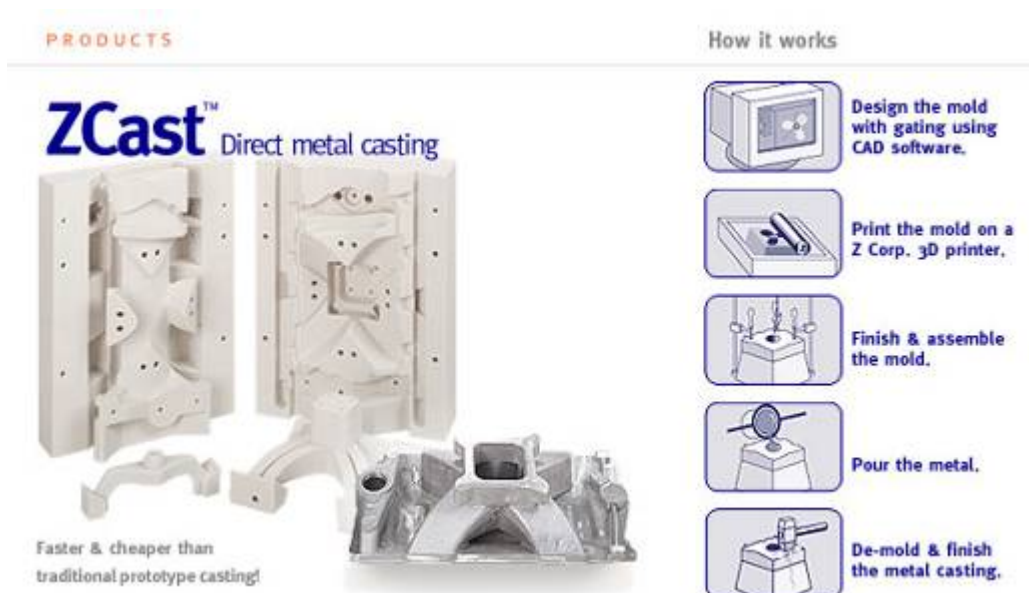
Примеры изделий, литейные формы для которых были изготовлены на 3D принтере
